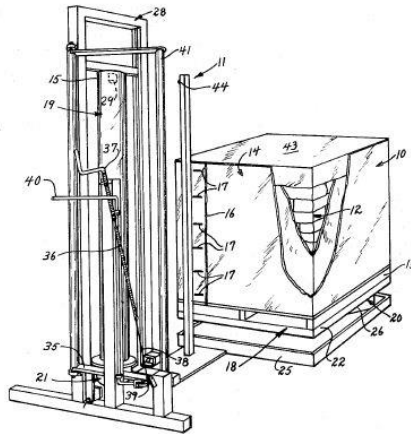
Proceso de envolver un paquete. Fuente: [80].
